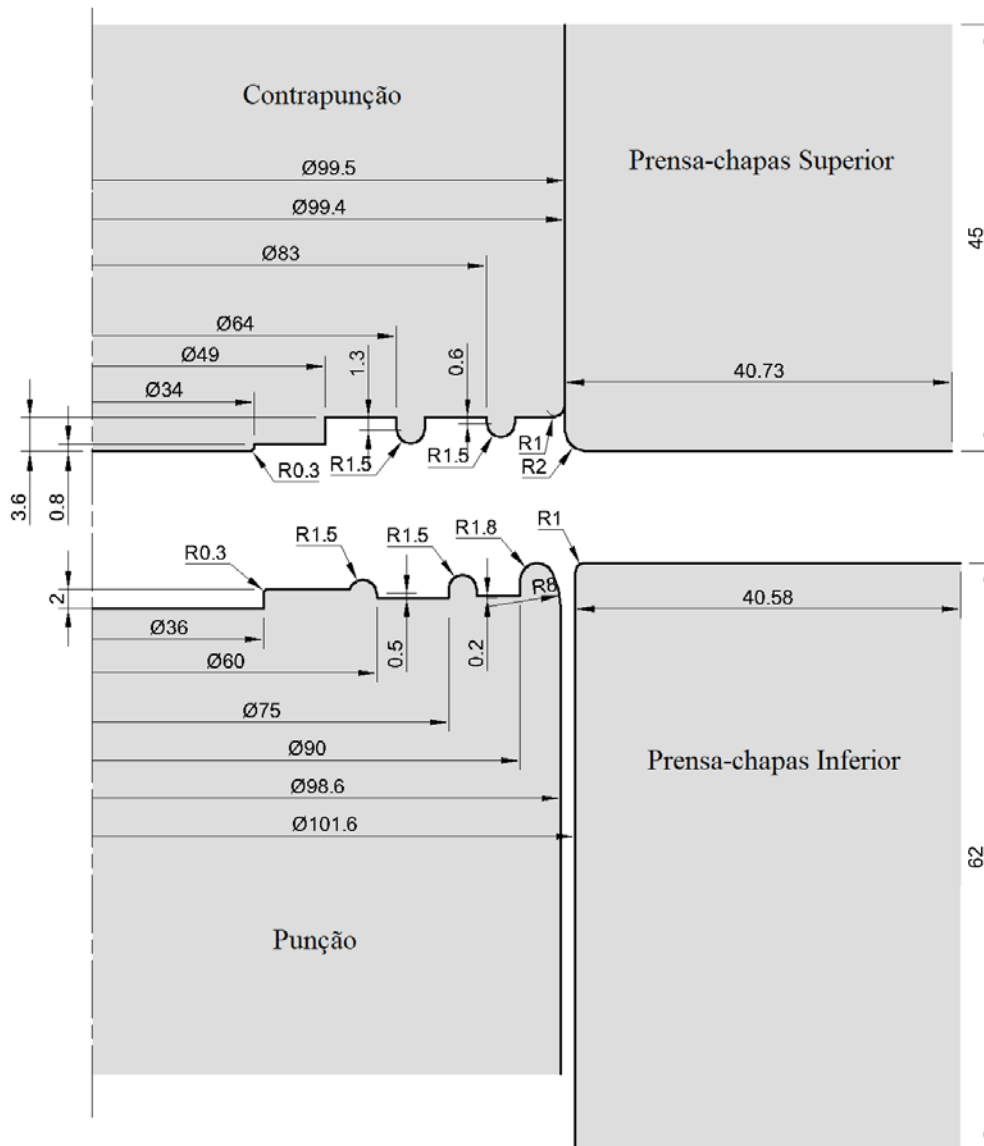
Conjunto do ferramental da estampagem profunda. Dimensões em mm.
